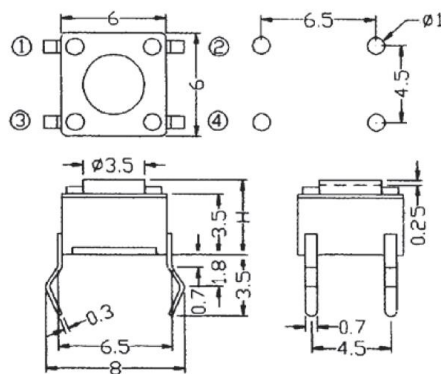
Габаритні розміри кнопки KLS7-TS6601-13.0-180
